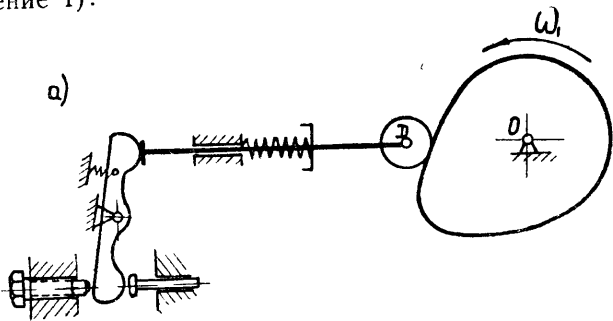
4. а) Схема кулачкового механизма выталкивателя
